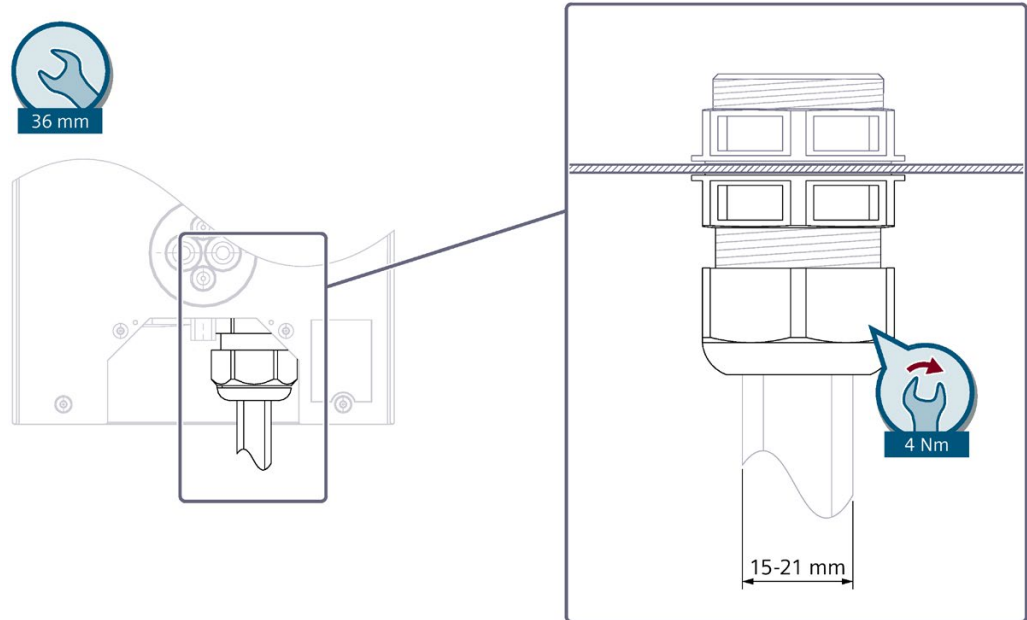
Einspeisung Wallbox 8EM1310-..0-....
